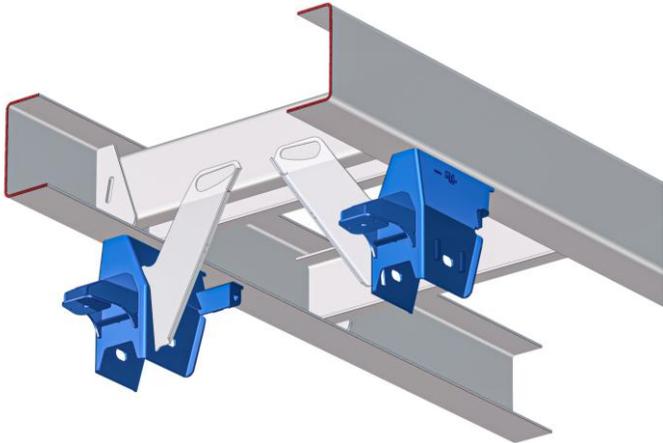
Reforço de ligação da travessa e suporte frontal – AirSuper e AirTop
